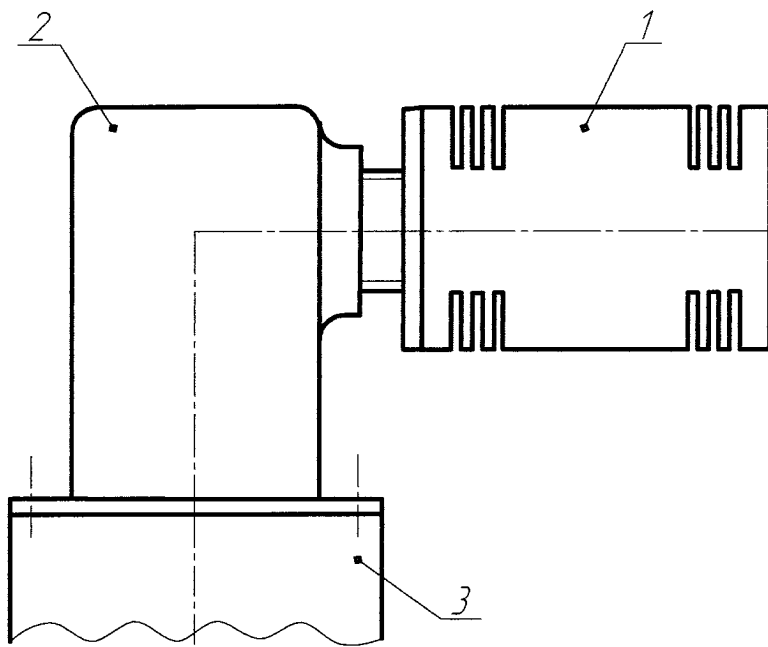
Конструктивная схема щелевого глушителя шума: 1 – глушитель; 2 – переходник; 3 – пневмораспределитель
